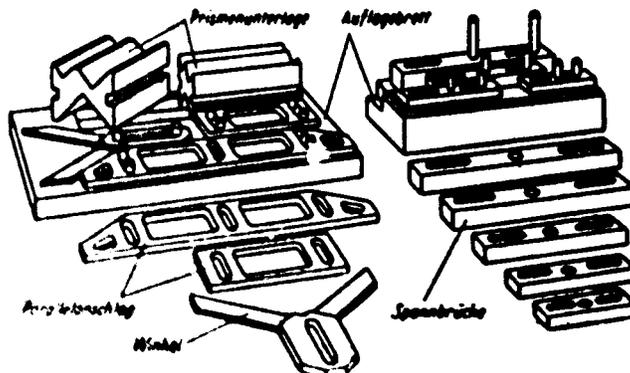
Parallel- und Winkelanschläge mit Prismenunterlage und Spannbrücken
